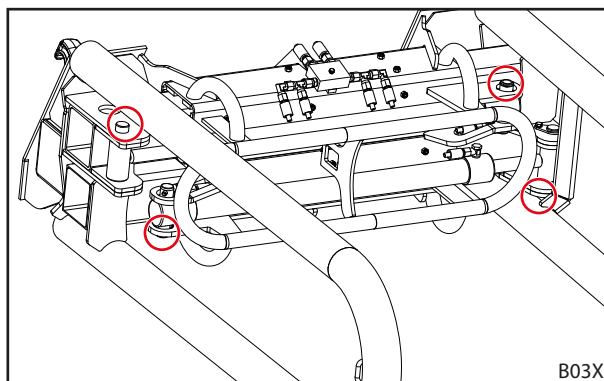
Точки смазки захвата для тюков в пленке Pro H
